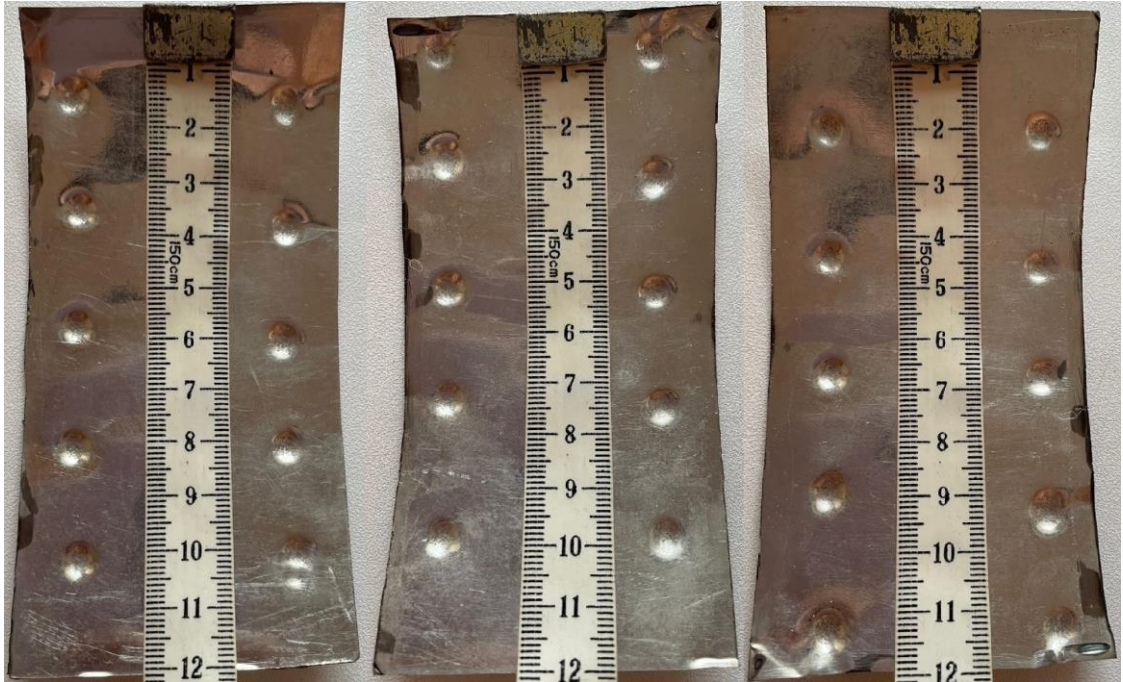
Общий вид и размеры пластин по длине после формообразования
